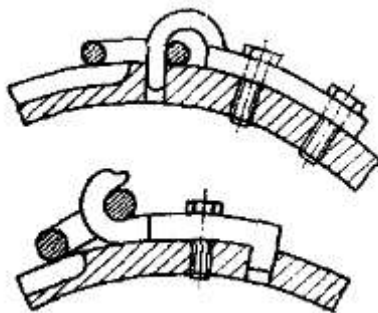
Крепление сварной цепи к барабану
